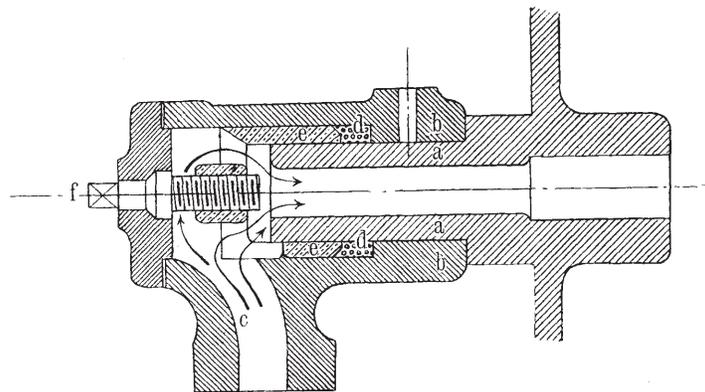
Schnitt durch das Lager einer Trockenmaschinentrommel.
